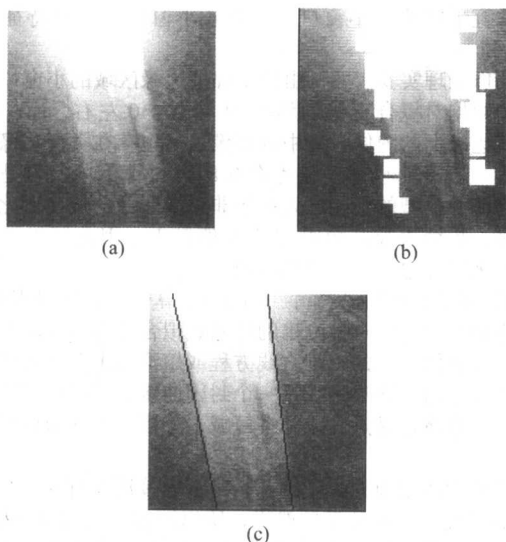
焊接过程中的焊缝图像处理
